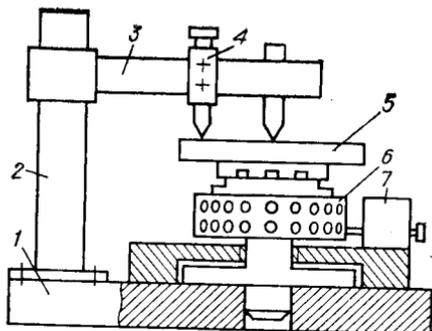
Приспособление для разметки отверстий во фланцах:
